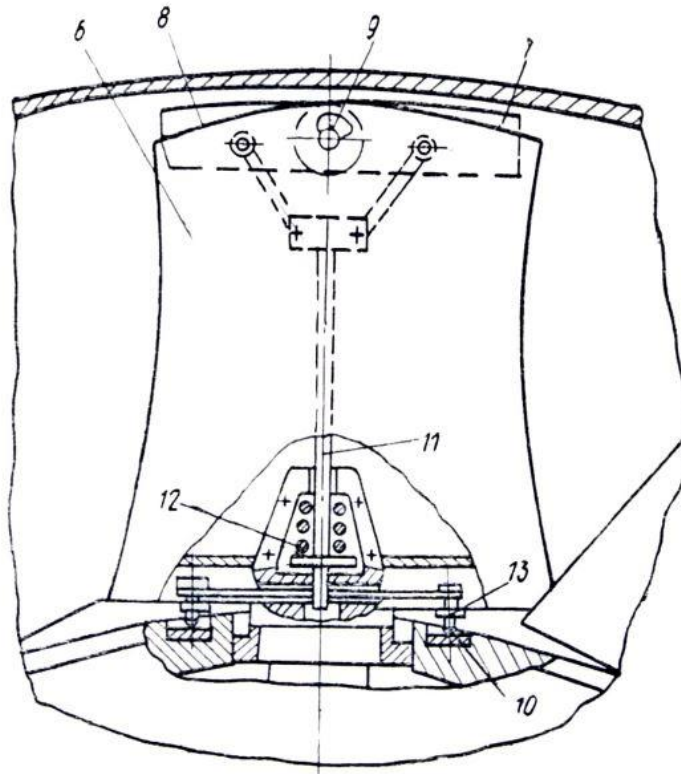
Схема лопатки із механізмом регулювання мінімального зазору.[8]
